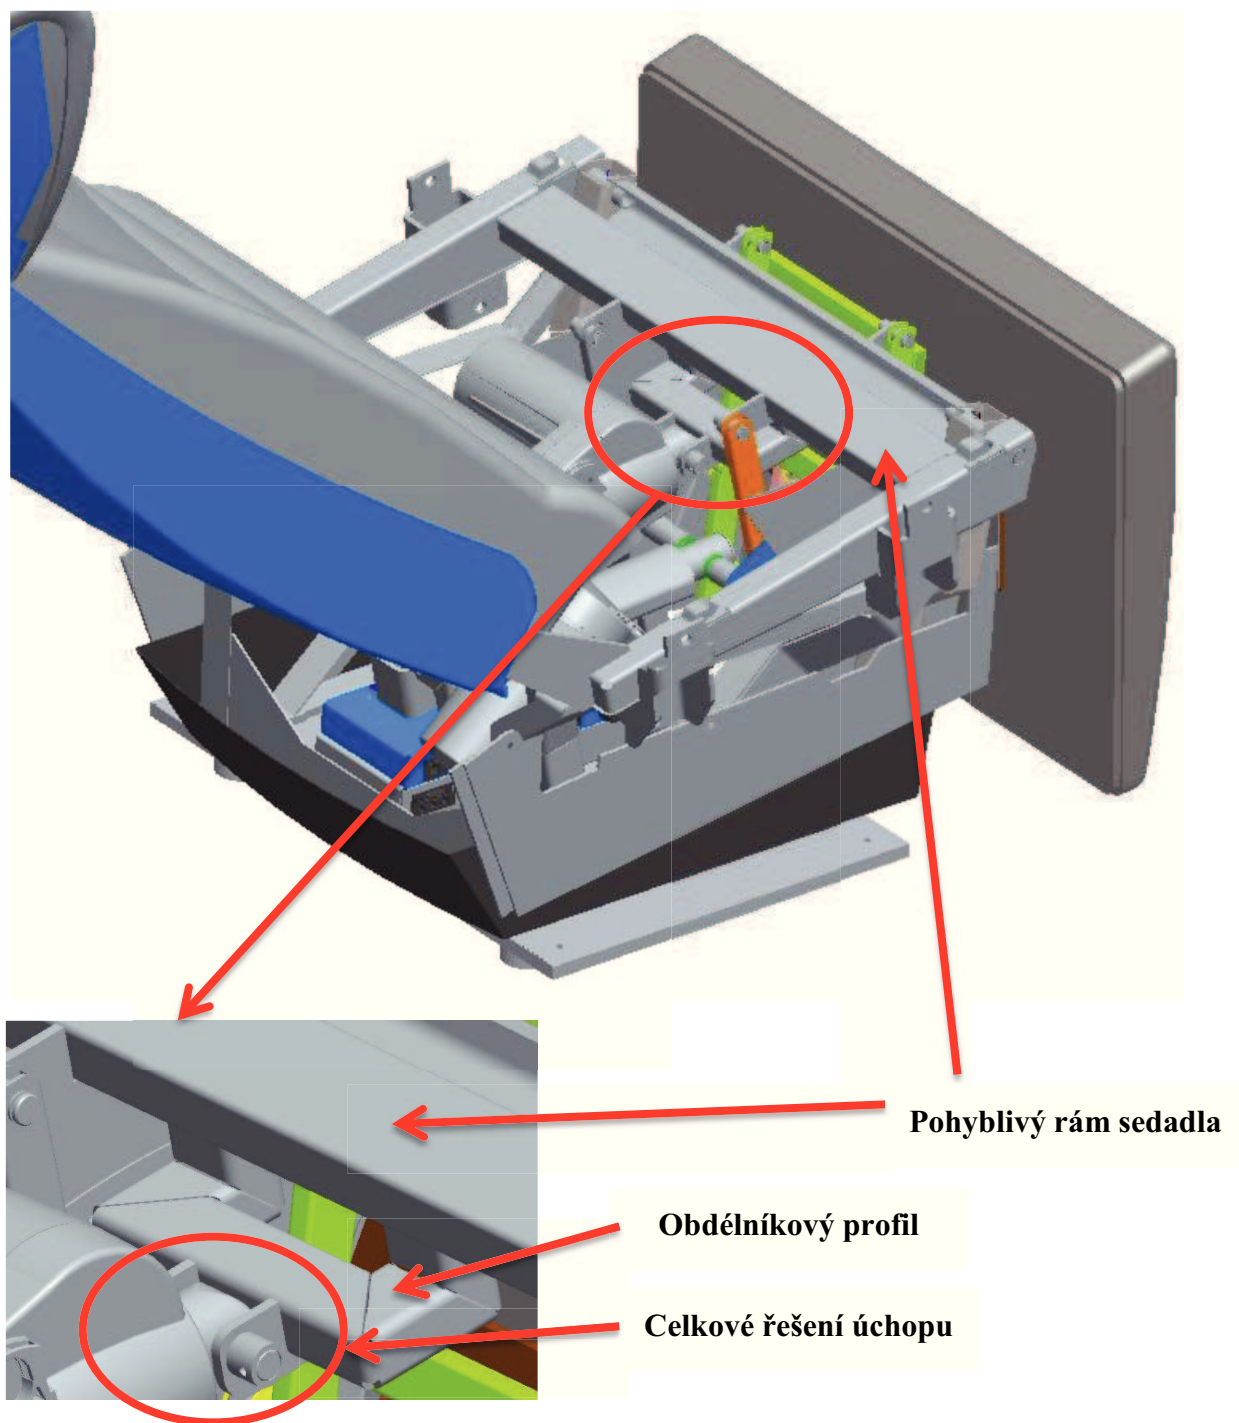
Tvar úchytu motoru Linak LA27 (14)
